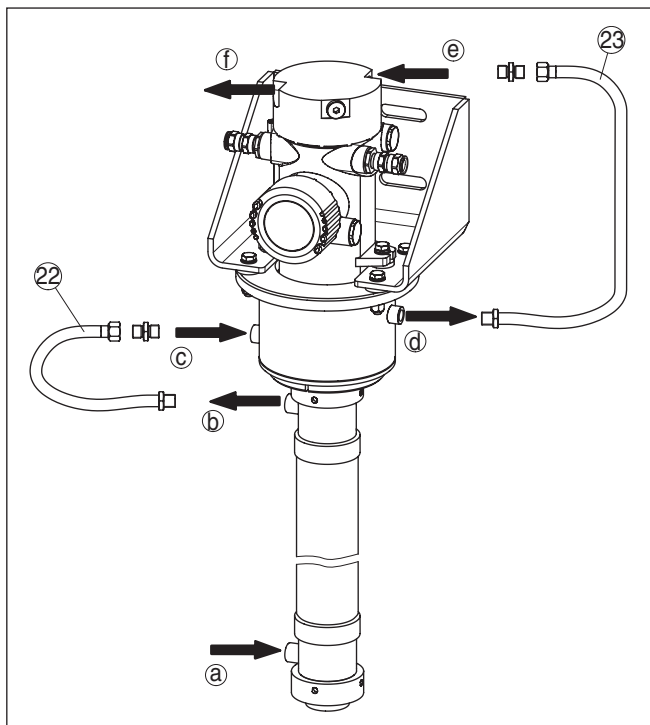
Направление течения охлаждающей жидкости (вертикальный монтаж, голова корпуса вверх)
